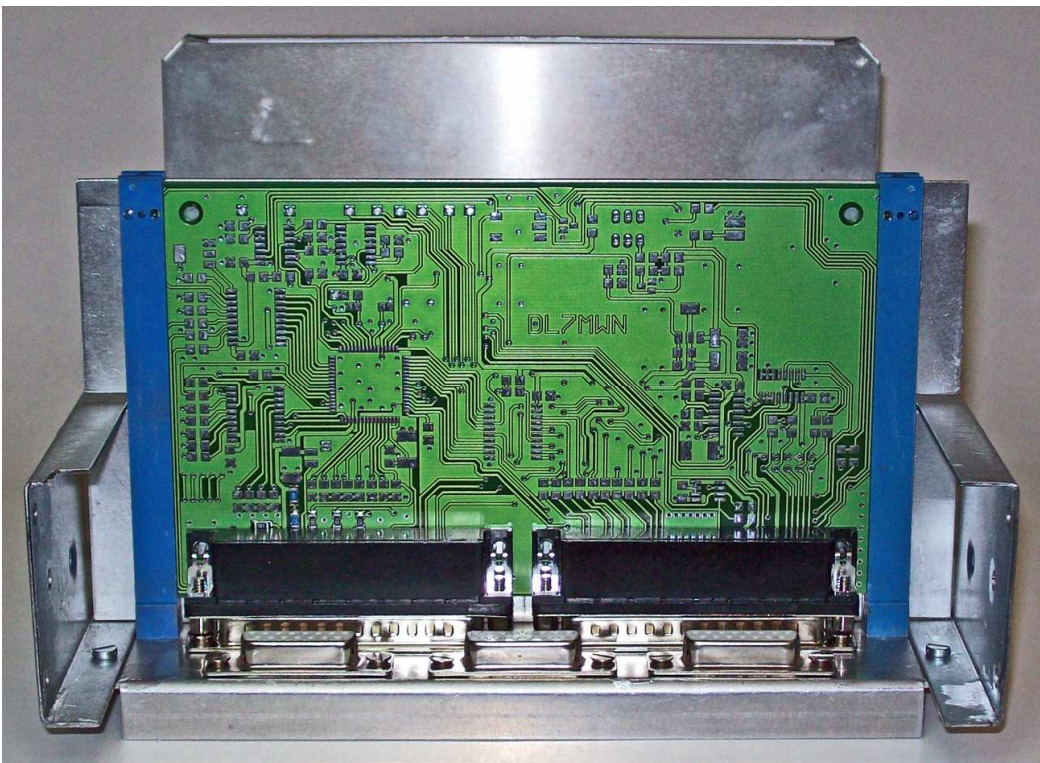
Gehäuseaufbau mit eingeschobenem, unbestücktem Steuerrechner
